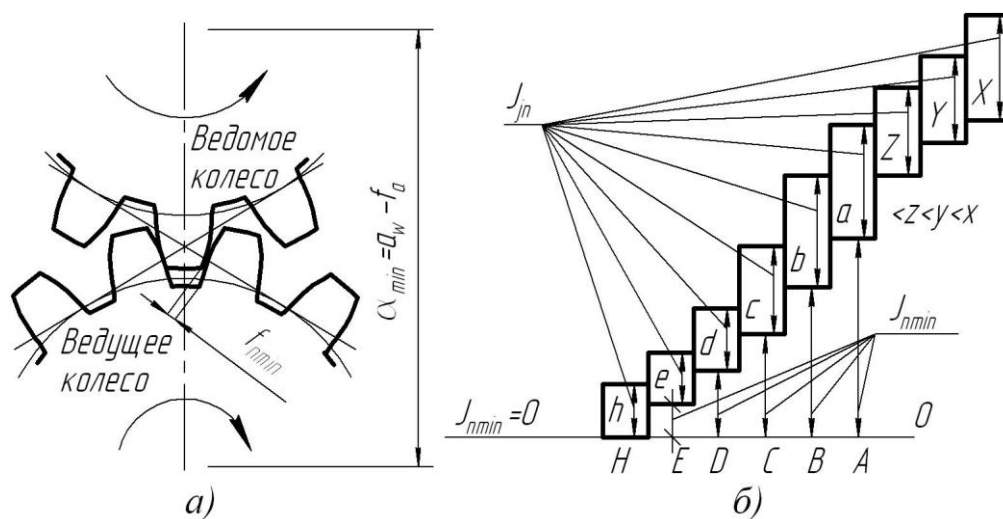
Боковой зазор (а) и виды сопряжений (б) зубчатой передачи
